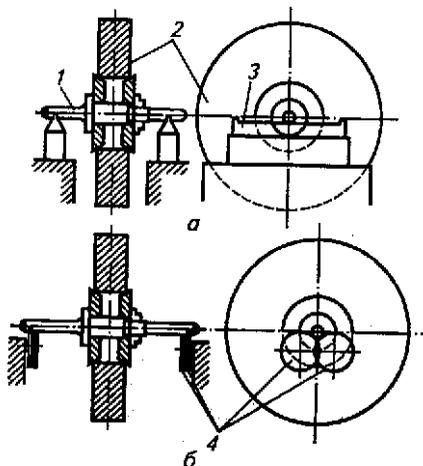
Схемы статической балансировки: а – на призмах; б – на роликах; 1 – оправка; 2 – детали; 3 – призма; 4 – дисковые ролики
